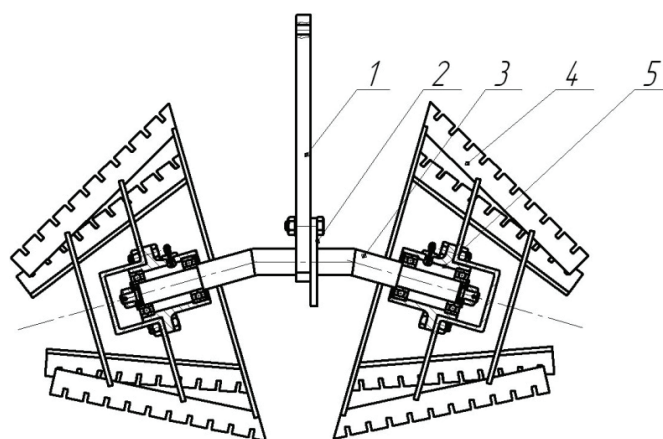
Сборный чертеж ротационного рыхлителя
